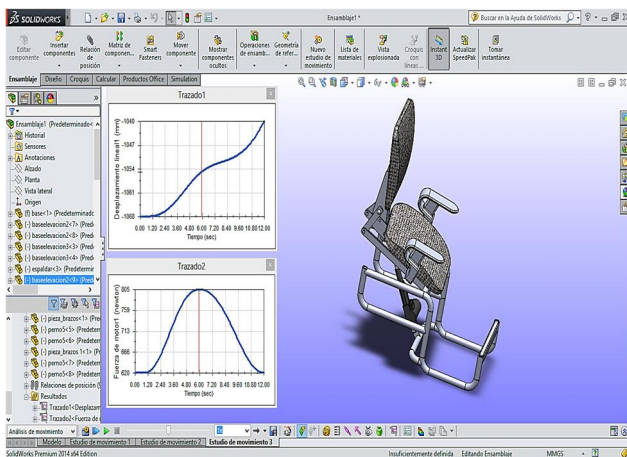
Diseño de ensamblaje de la silla bipedestadora
